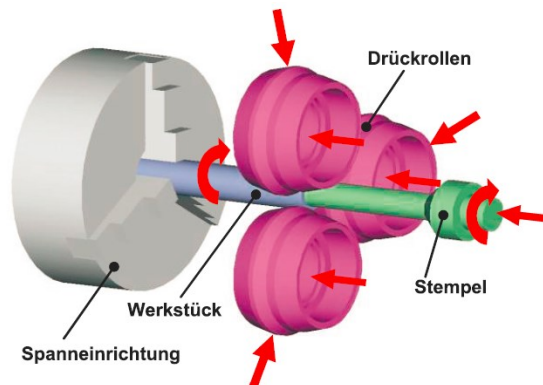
Prinzip des Bohrungsdrückens.⁶⁰
